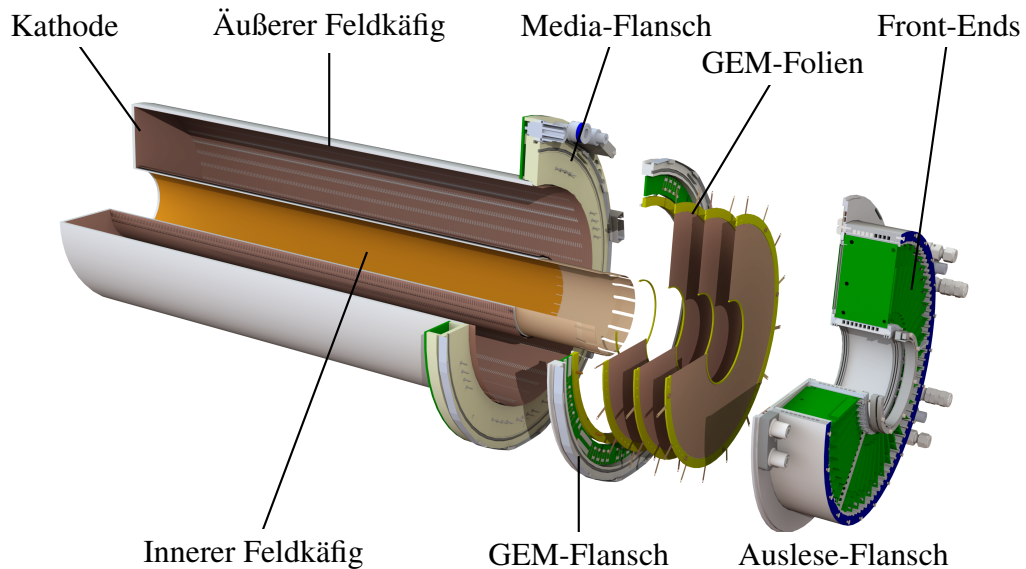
Explosionsansicht des TPC-Prototypen aus [100].
